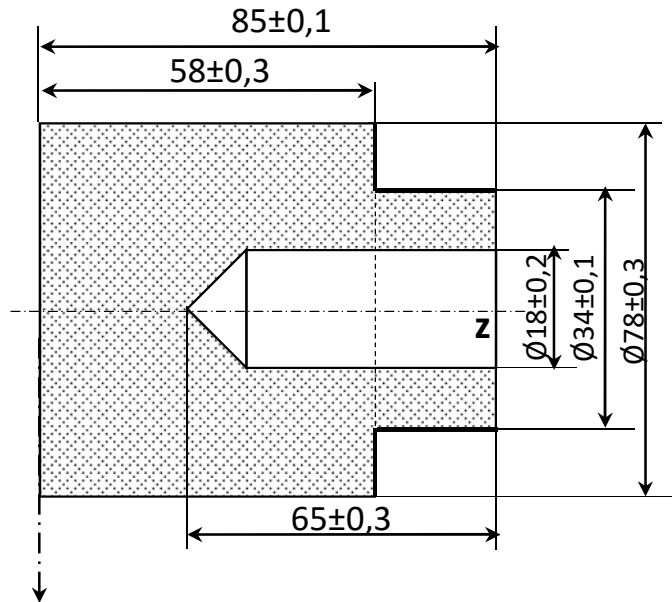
Dessin de définition d'une pièce mécanique destinée au tournage.
